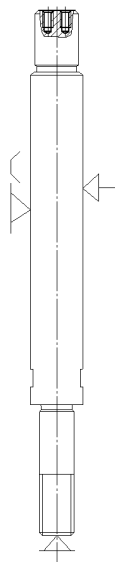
Схема базування та закріплення стійки при свердлуванні
